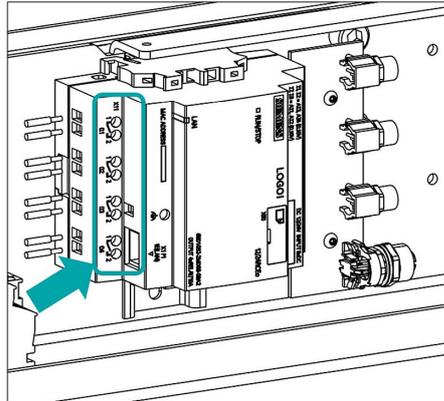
, Steuerung: Verschraubung Leitungen Mehrstockklemmen
